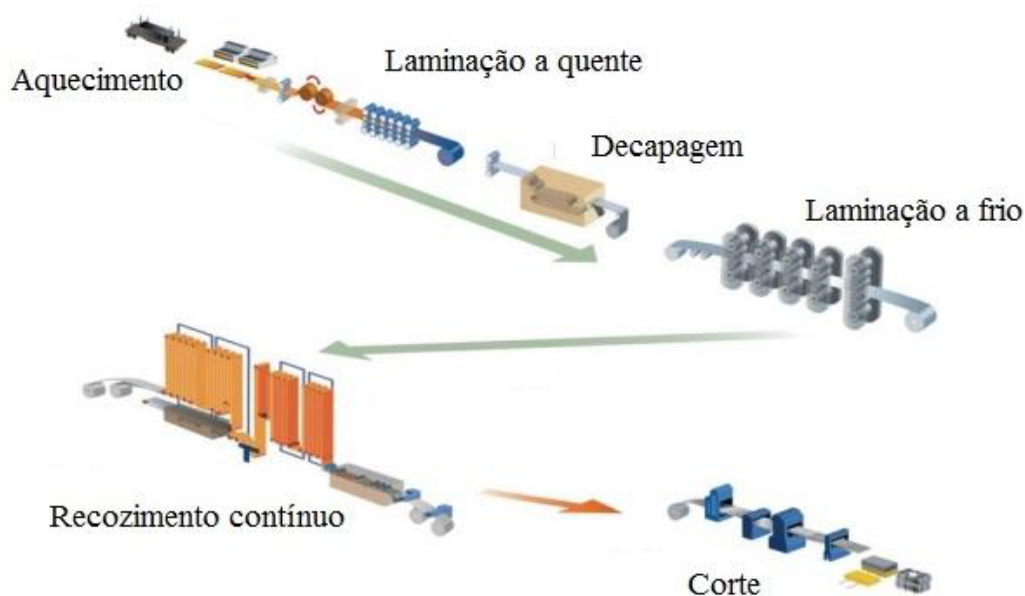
Layout de planta de produção de aço laminado a frio. (ROCHA, 2014 Apud GRANBOM, 2010).
